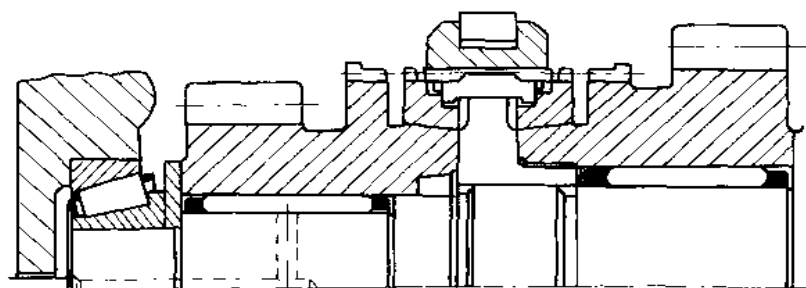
一种采用塑料保持架的滚针轴承的轿车变速器自由齿轮支承
